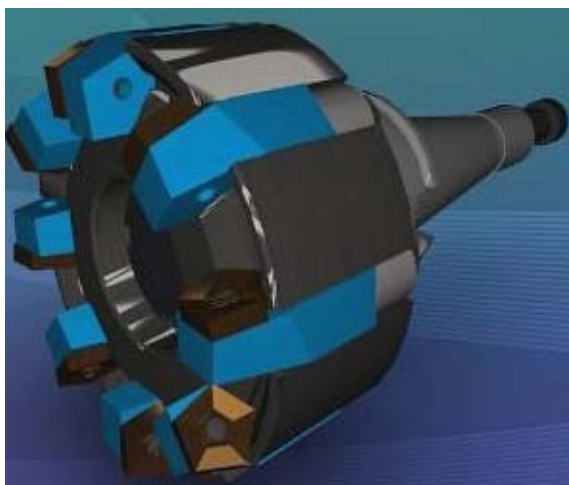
Рендерінг інструментального блоку для фрезерування
